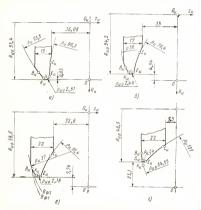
Профили дисковой фрезы для обработки винтовых канавок у цилиндрических фрез, рассчитанные при различных значениях параметров ее установки
